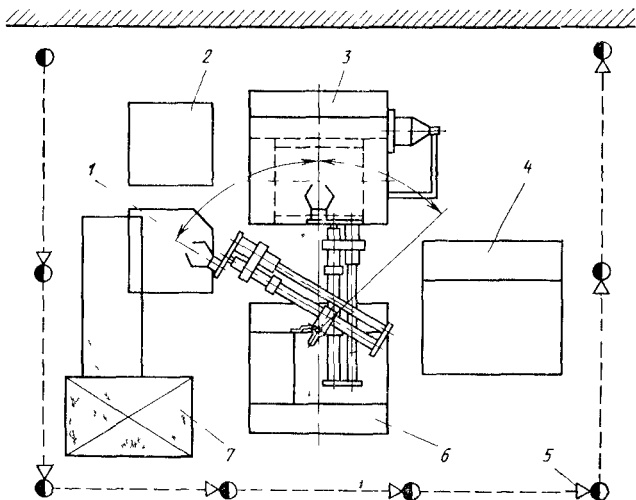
Компоновка РТК на базе чеканочного пресса
